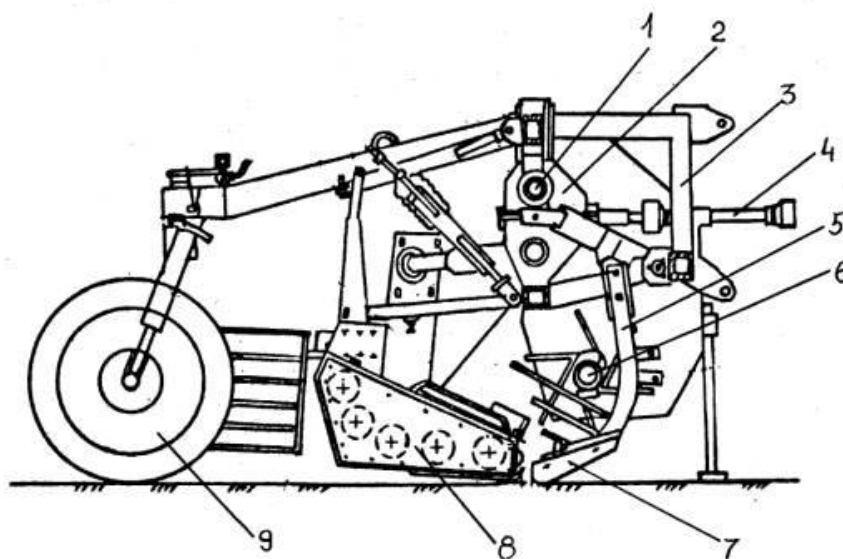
Конструктивна схема навісної машини КВЦБ-1,2 з лемішними віброкопачами [19]: 1 – ексцентриковий механізм; 2 – редуктор; 3 – рама; 4 – карданна передача; 5 – викопуючий пристрій; 6 – бітер-проштовхувач; 7 – лемеші; 8 – шнековий очищувач; 9 – опорні колеса.
